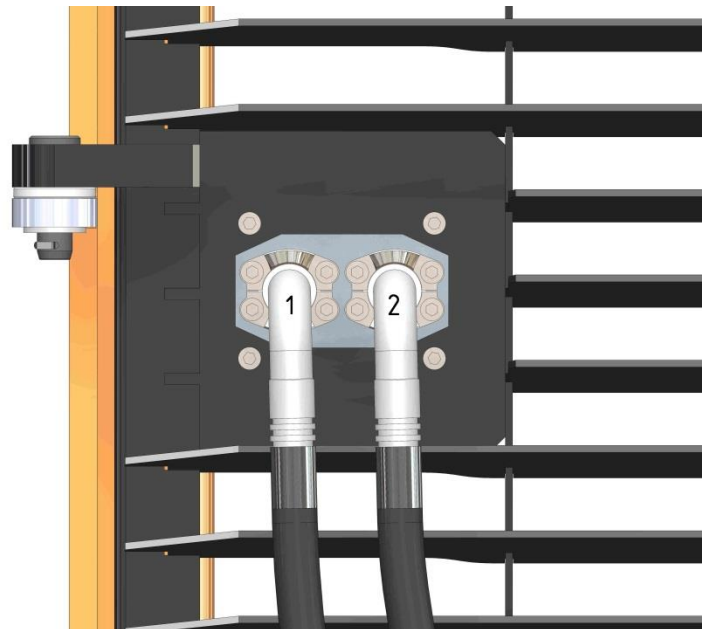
Монтаж гидрOLIний перекоса отвала.
